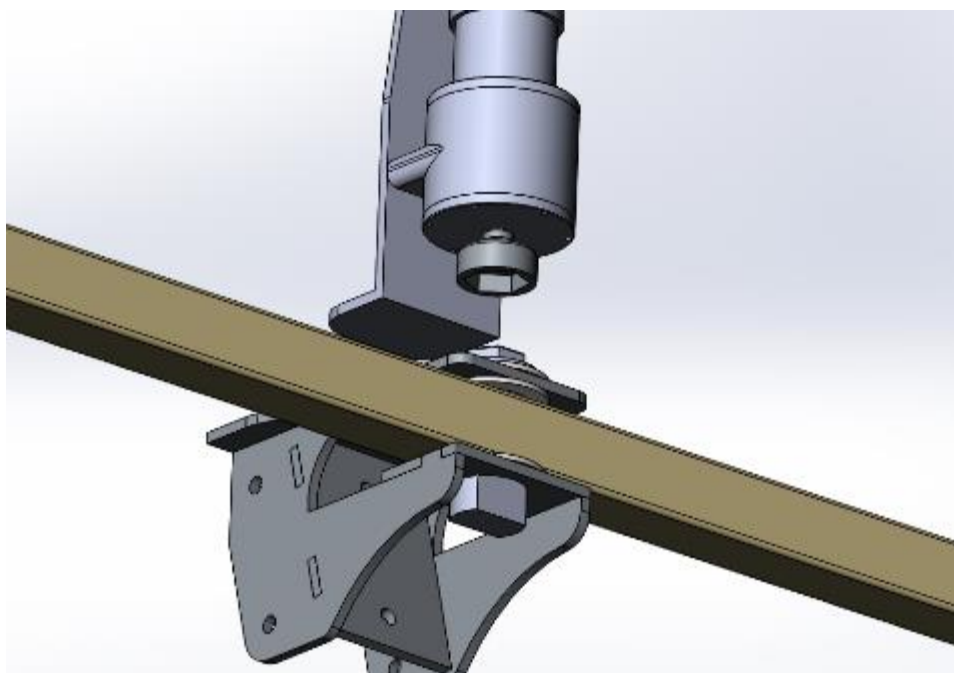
Площадка стабилизатора и привод на кронштейне, вид снизу
